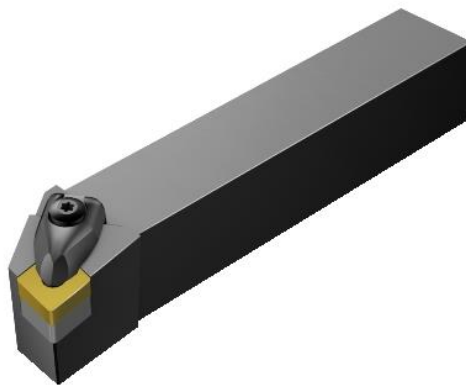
Різець прохідний упорний DCLN 2525M 16
